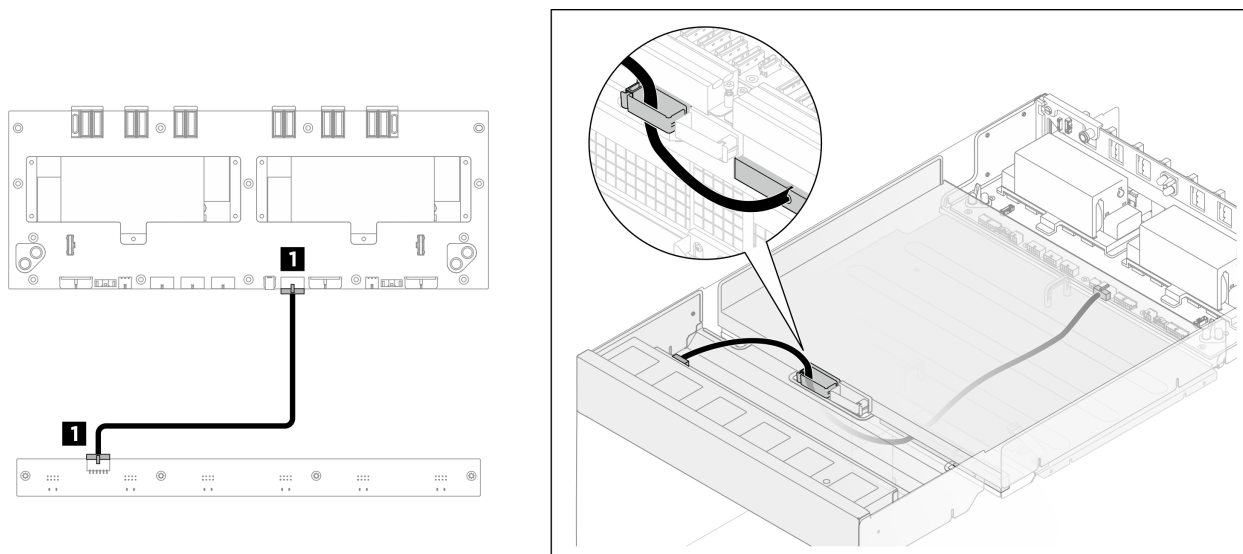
Disposición de los cables de la placa de control del ventilador frontal
